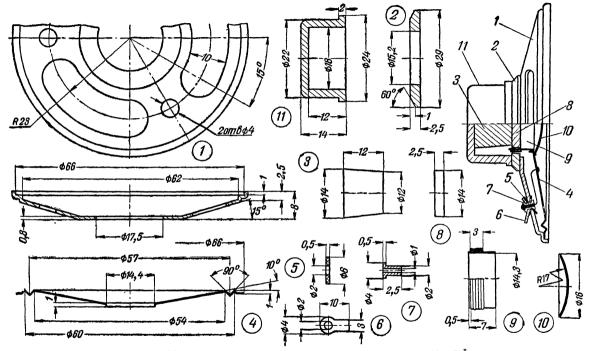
Конструкция громкоговорителя и размеры его деталей.
